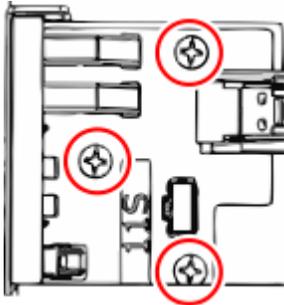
Schrauben der Steuerkonsole wieder anbringen
